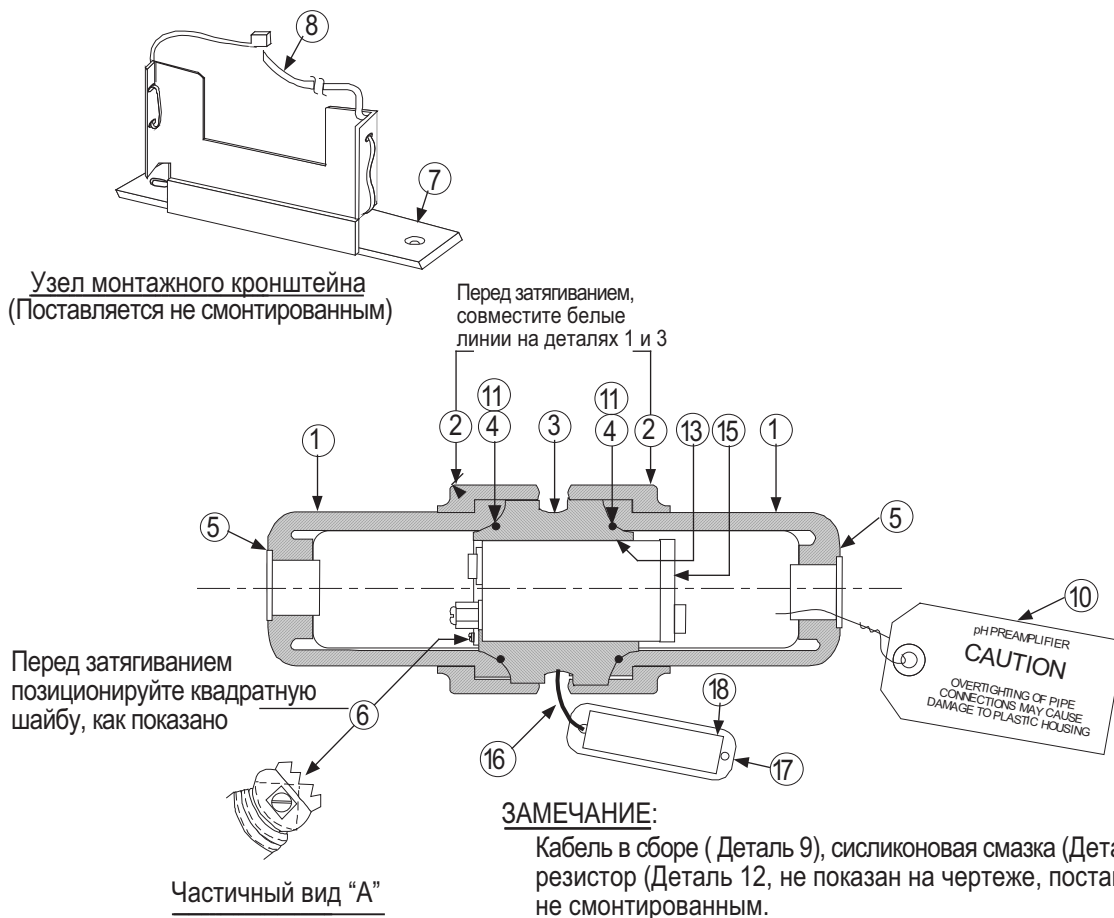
Монтажный и габаритный чертеж распределительной коробки 31316260.
